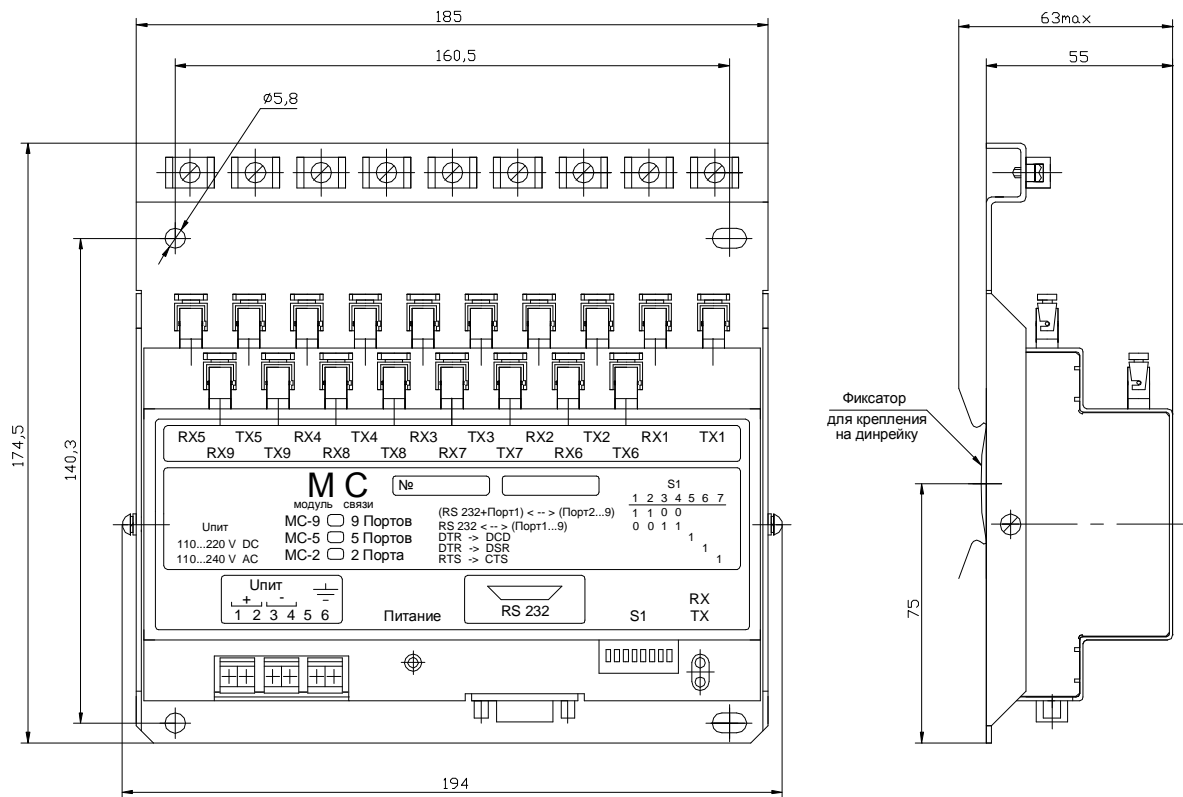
Внешний вид, габаритные и установочные размеры модулей
